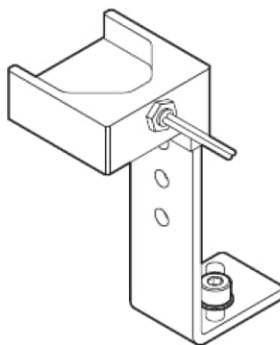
Лоток подачі заготовки з оптичним датчиком
